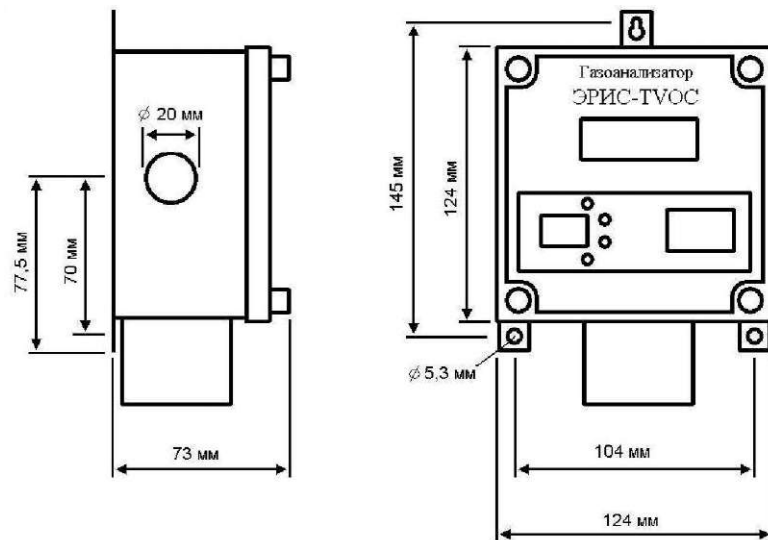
Габаритные и присоединительные размеры датчика-газоанализатора ЭРИС-TVOC
